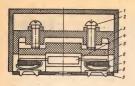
Контактирующая головка съемной конструкции для корпусов планарного типа [85]
